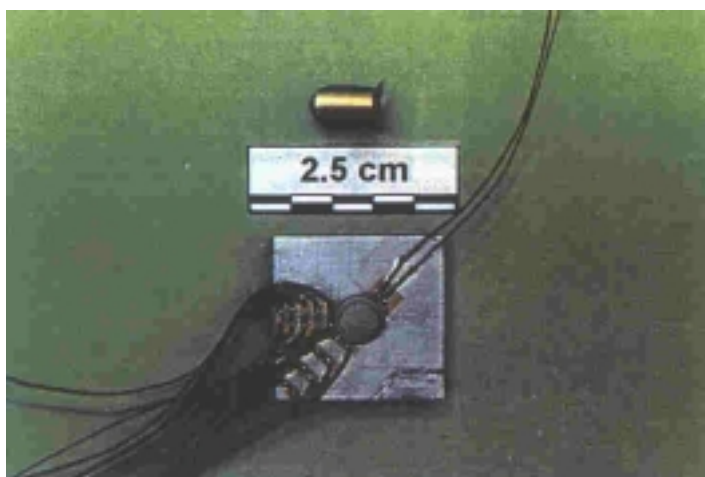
Éprouvette carrée $L=20 \text{ mm}$ après rivetage.
